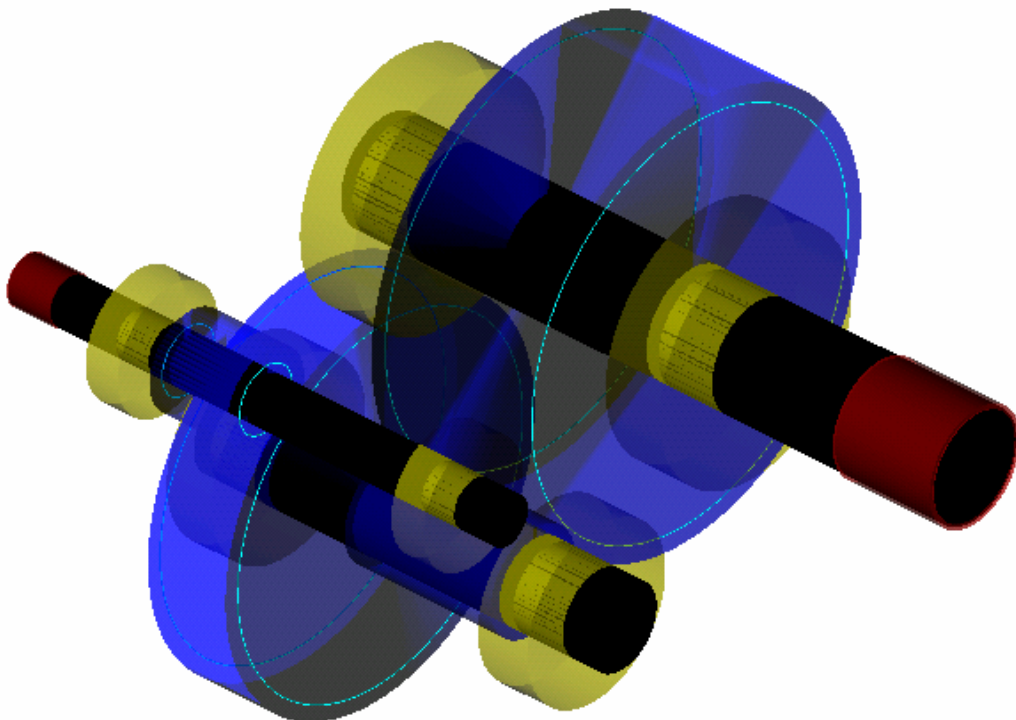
Getriebe mit 45° Winkel zwischen den Wellen. Blau: Zahnräder, Schwarz: Wellen, Gelb: Wälzlager, Rot: Kupplungen
